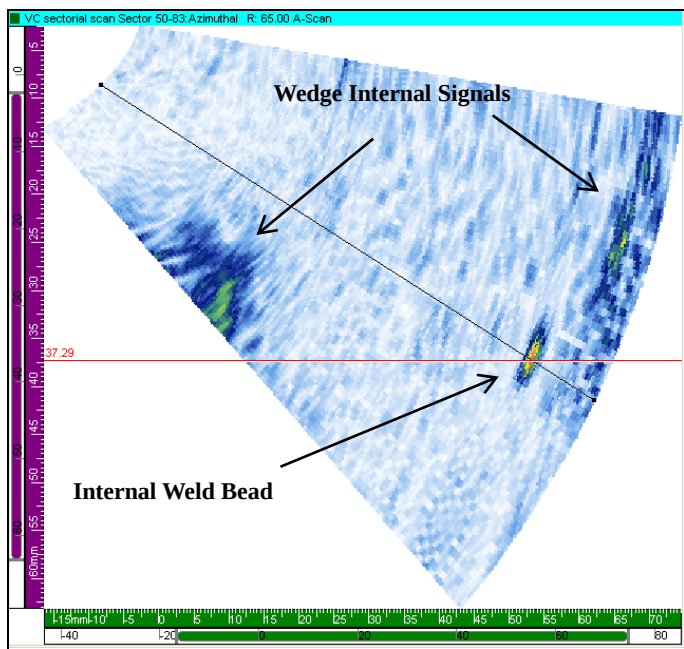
IMAGEN DE UNA UNIÓN BF EN UNA TUBERÍA DE PE DE 355MM SIN DEFECTOS
